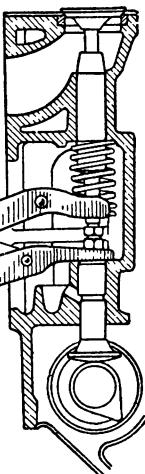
Приспособление для сжатия пружины клапанов при разборке
